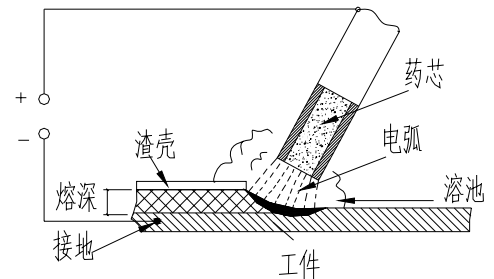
焊条电弧焊（手焊）原理示意图
